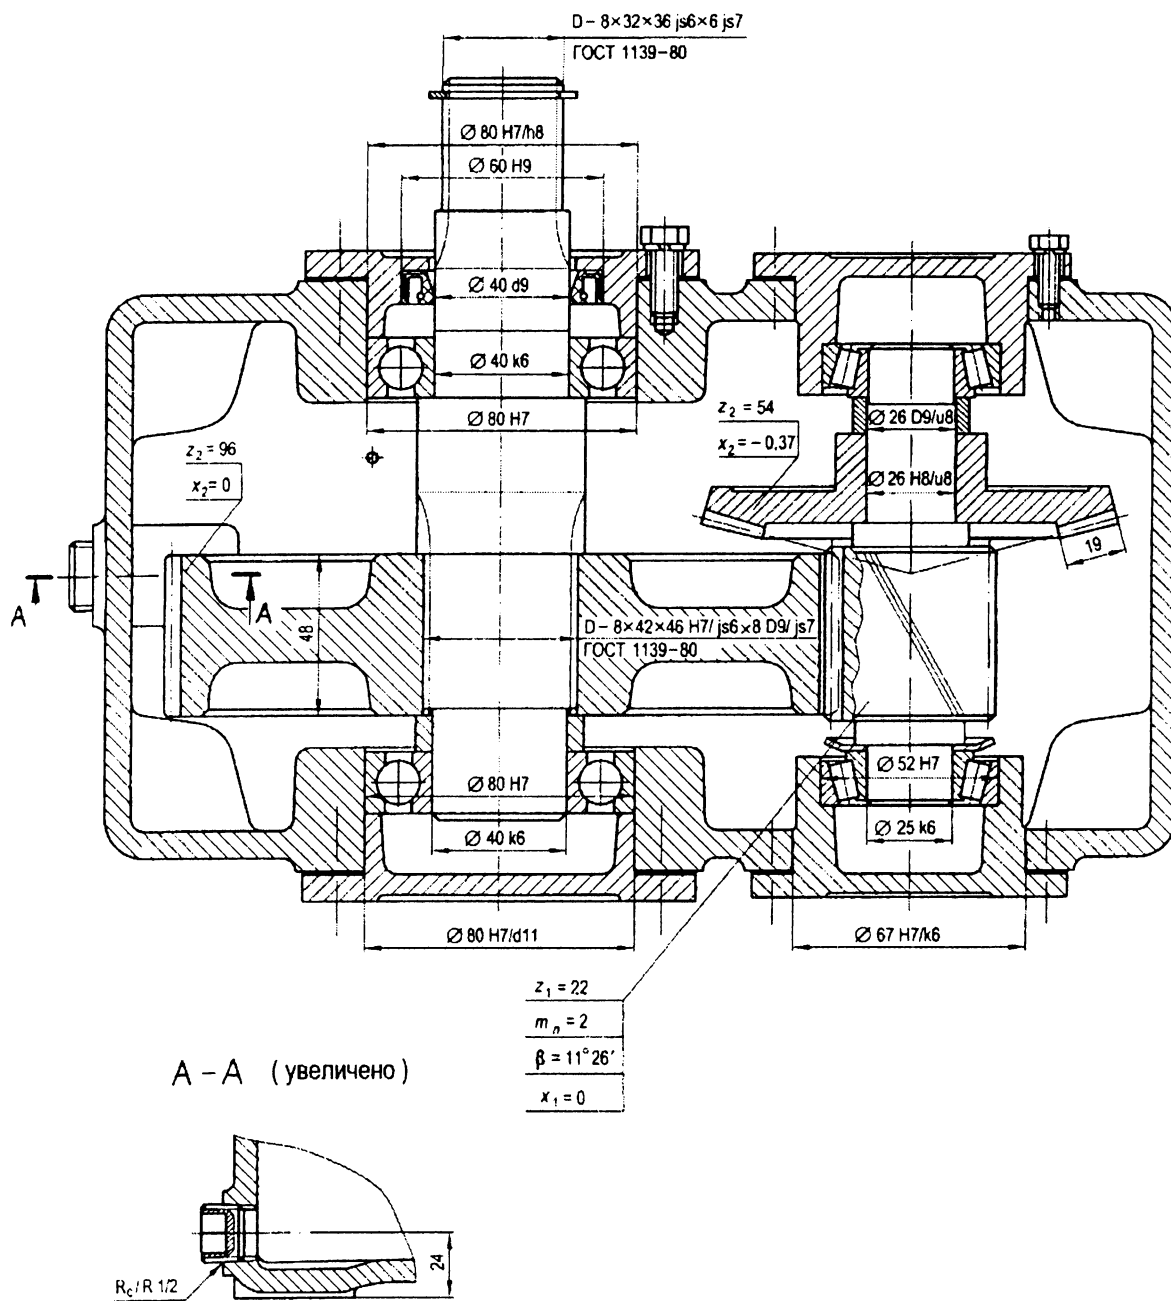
Пример конструкции тихоходного вала коническо-цилиндрического зубчатого редуктора без разъема корпуса и вертикально расположенным быстроходным валом [1]
